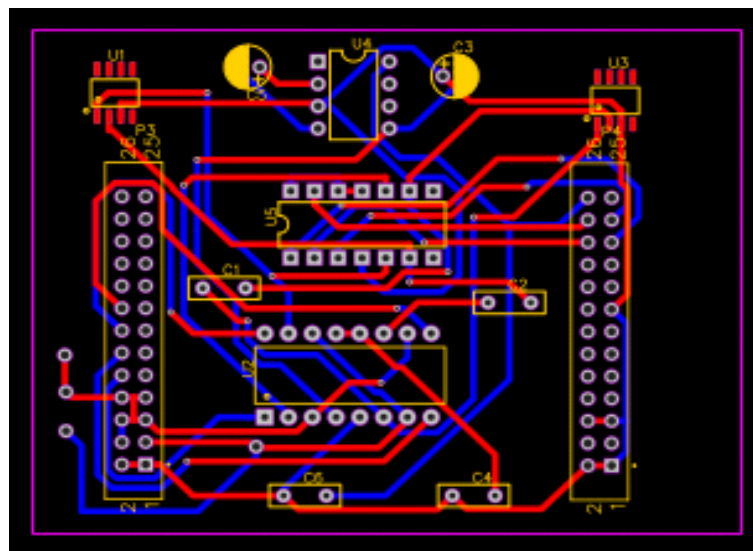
Schéma du PCB de la carte de TP 1 généré par EASYEDA
